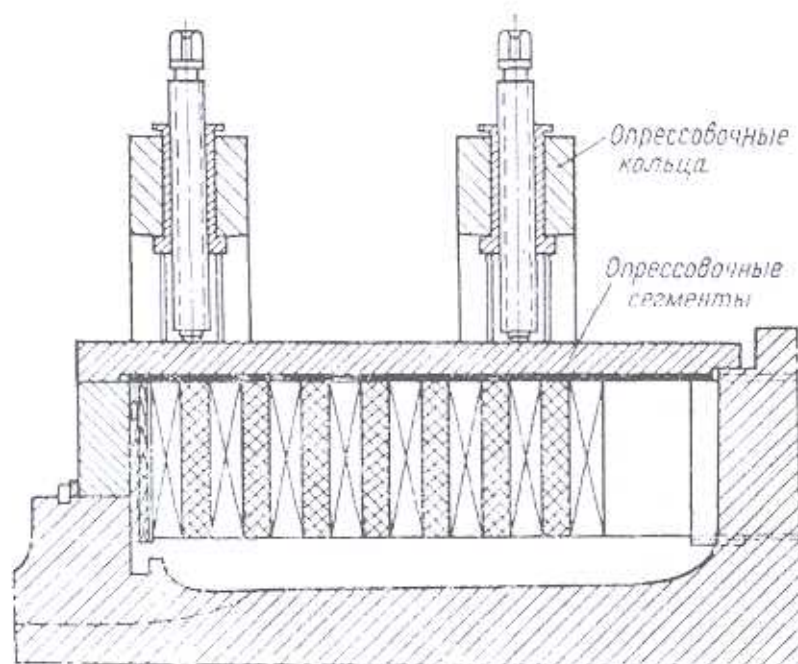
Опрессовка лобовых частей обмотки ротора
